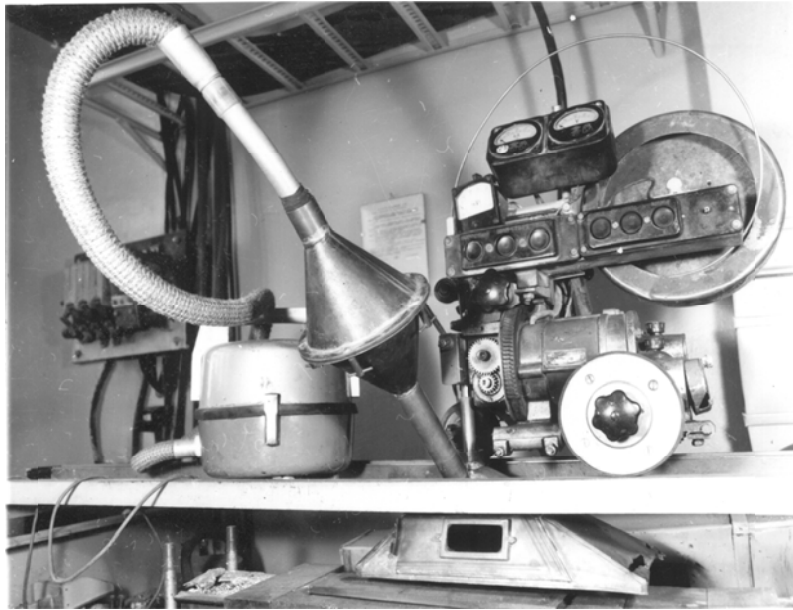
Стенд для отбора проб СА при автоматической сварке под флюсом
